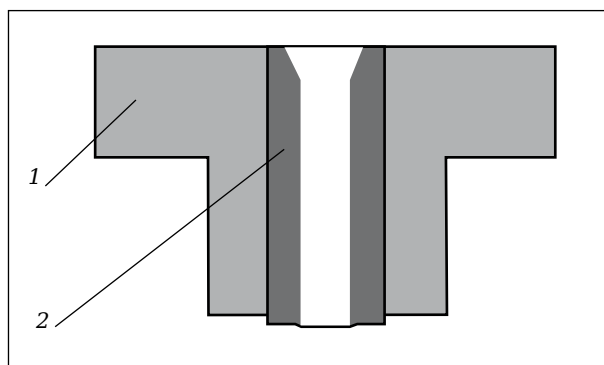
Стакан-дозатор CNC с удлиненной втулкой: 1 — основа; 2 — втулка
